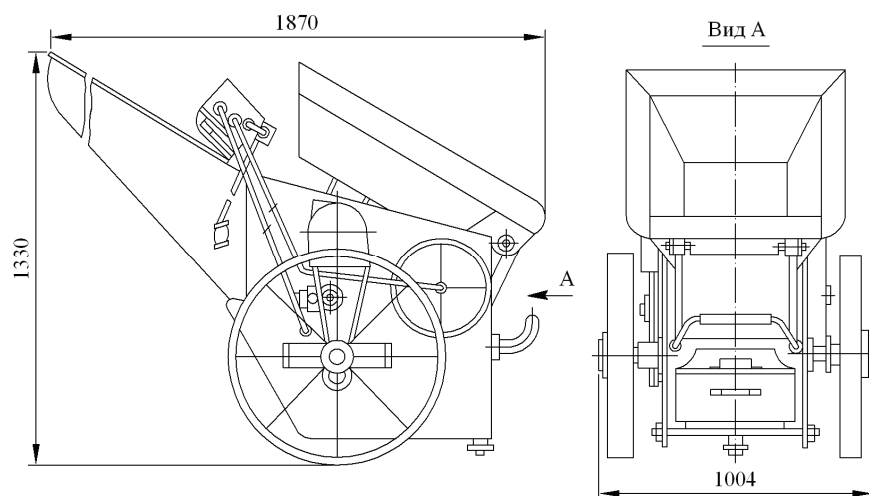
Общий вид землеприготовителя передвижного барабанного модели 126А
